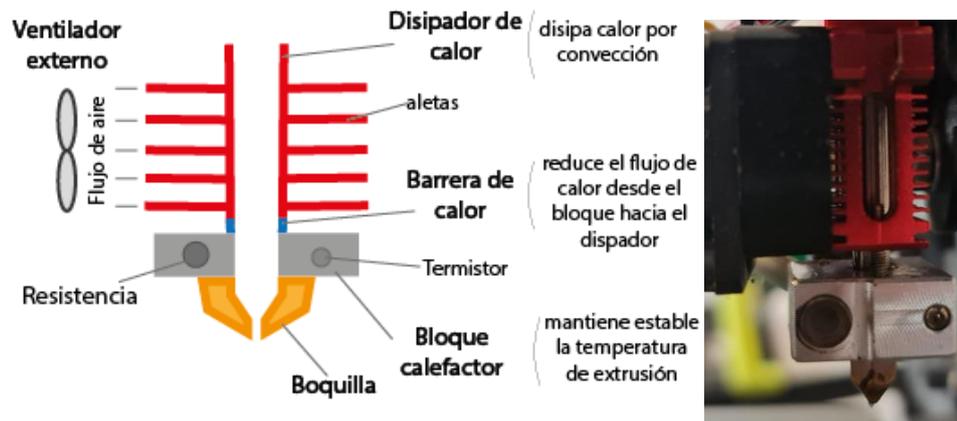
Estructura y partes de un extrusor estándar de impresión por FDM a la izquierda; Imagen real del extrusor de la impresora.
